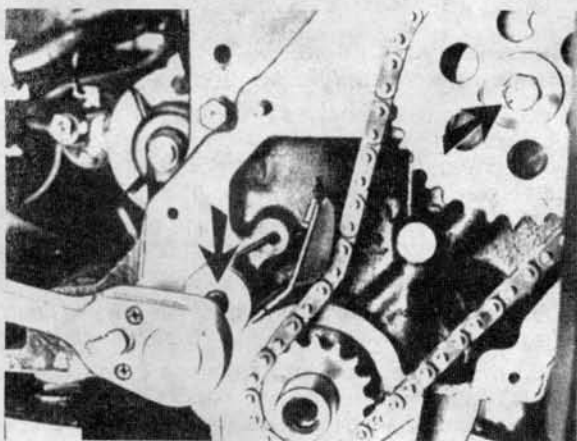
Снятие цепи механизма газораспределения двигателя В13/В14
